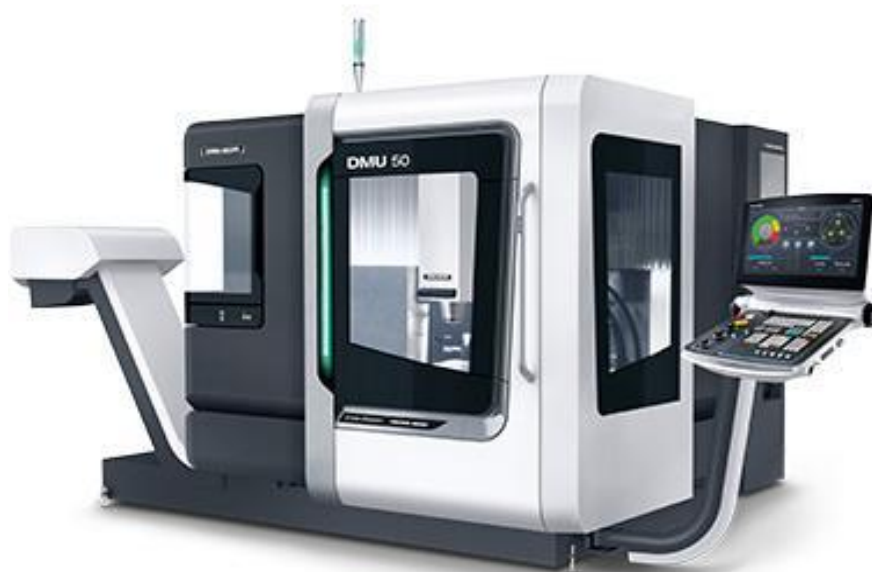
Обрабатывающий центр с ЧПУ DMU 50
